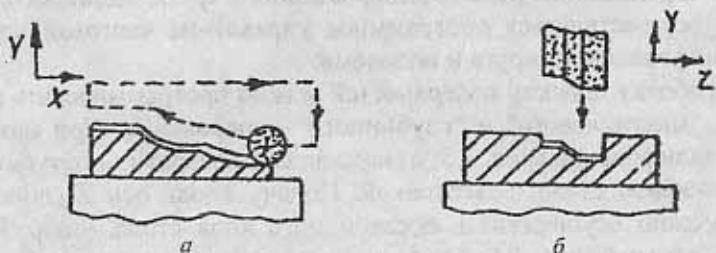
Обработка криволинейных поверхностей на плоскошлифовальных станках с ЧПУ
